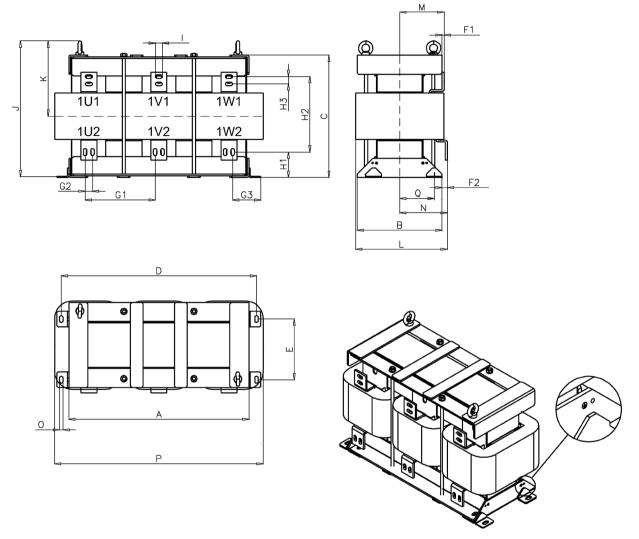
Габаритный чертеж сетевого дросселя 6SL3000-0EH41-4AA0
